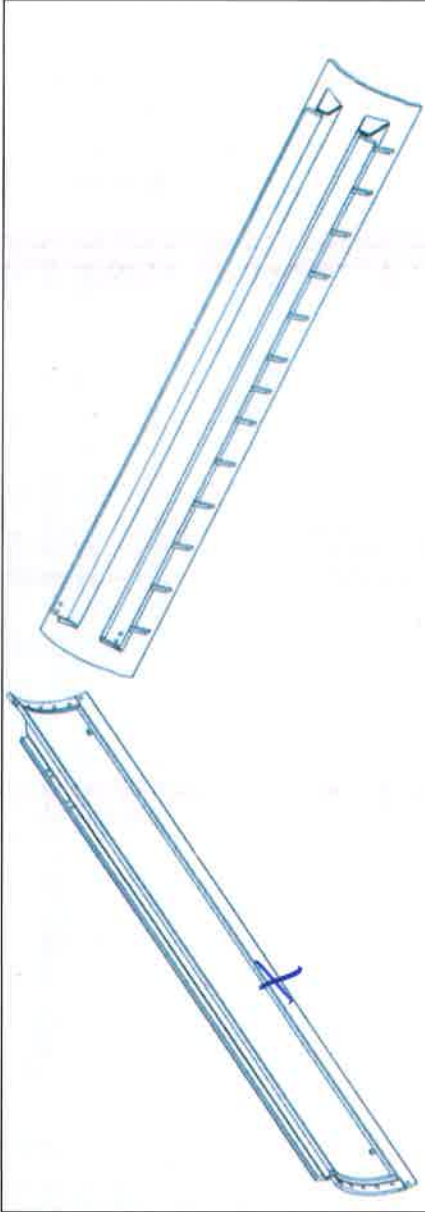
Revisar fisuras, marcas de golpes, desgaste anormal en las estructuras
